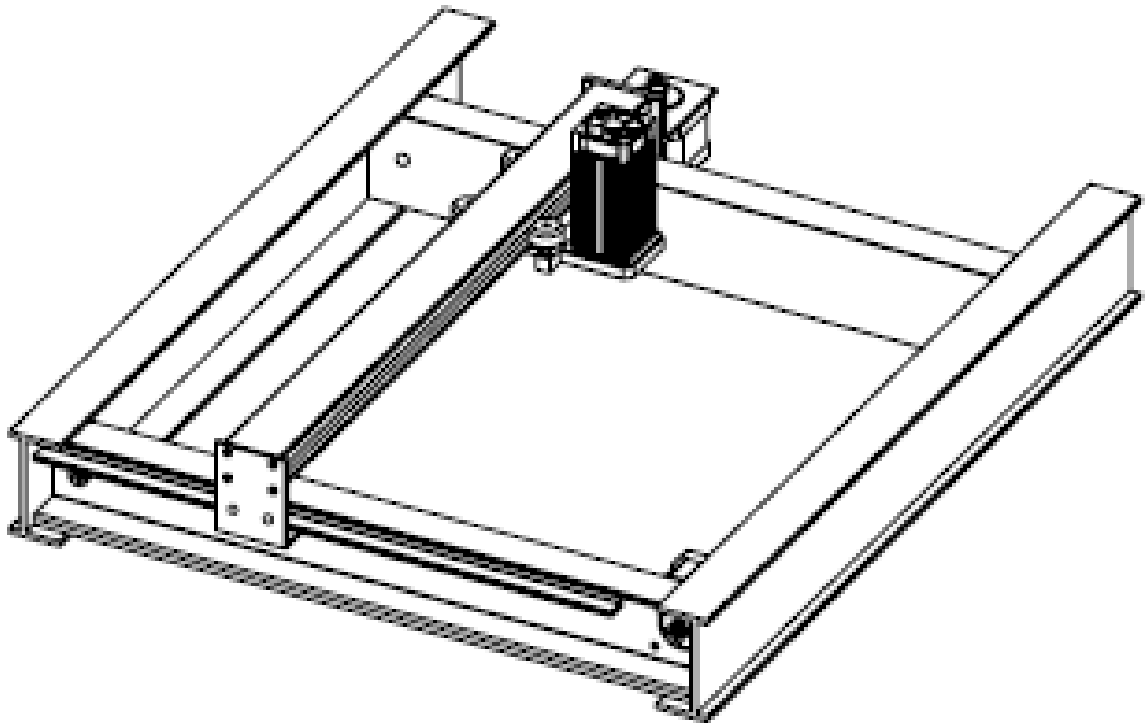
Загальний вигляд установки для лазерної різки матеріалів
